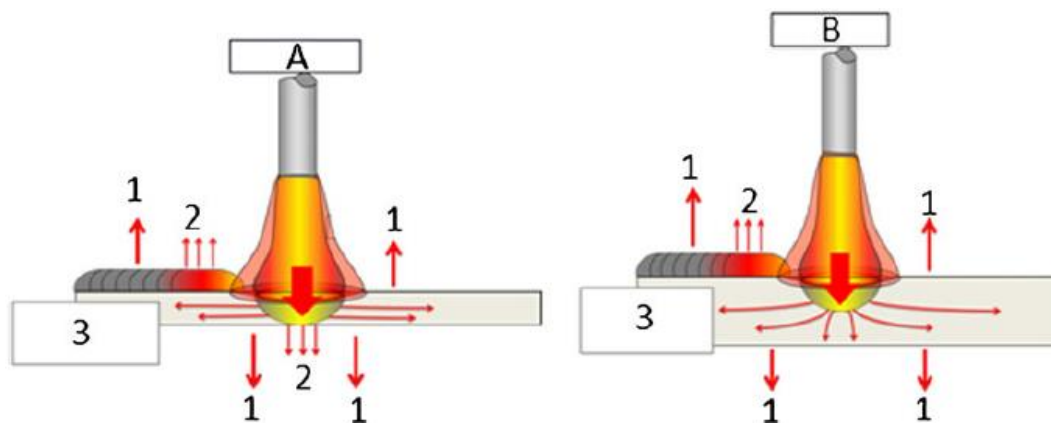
Transferência de calor na peça durante a soldagem. (a) Soldagem MIG/MAG com penetração total e (b) soldagem MIG/MAG com penetração parcial
